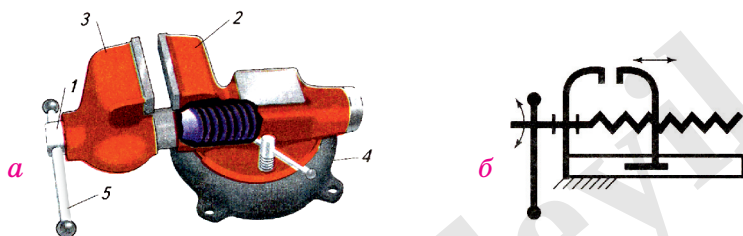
Тиски: а – устройство тисков (1 – винт, 2 – неподвижная губка, 3 – подвижная губка, 4 – опорная плита, 5 – рукоятка); б – схема тисков
